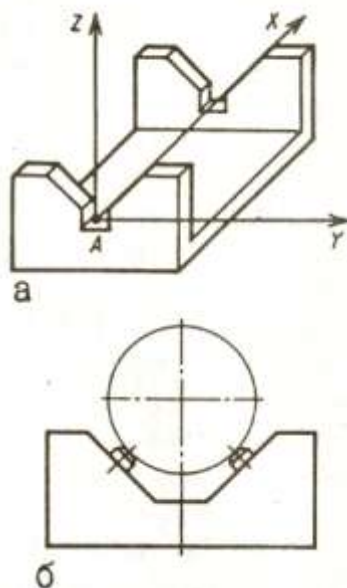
Призмы: а- с выемкой для установки длинных заготовок; б- с точечными опорами.
